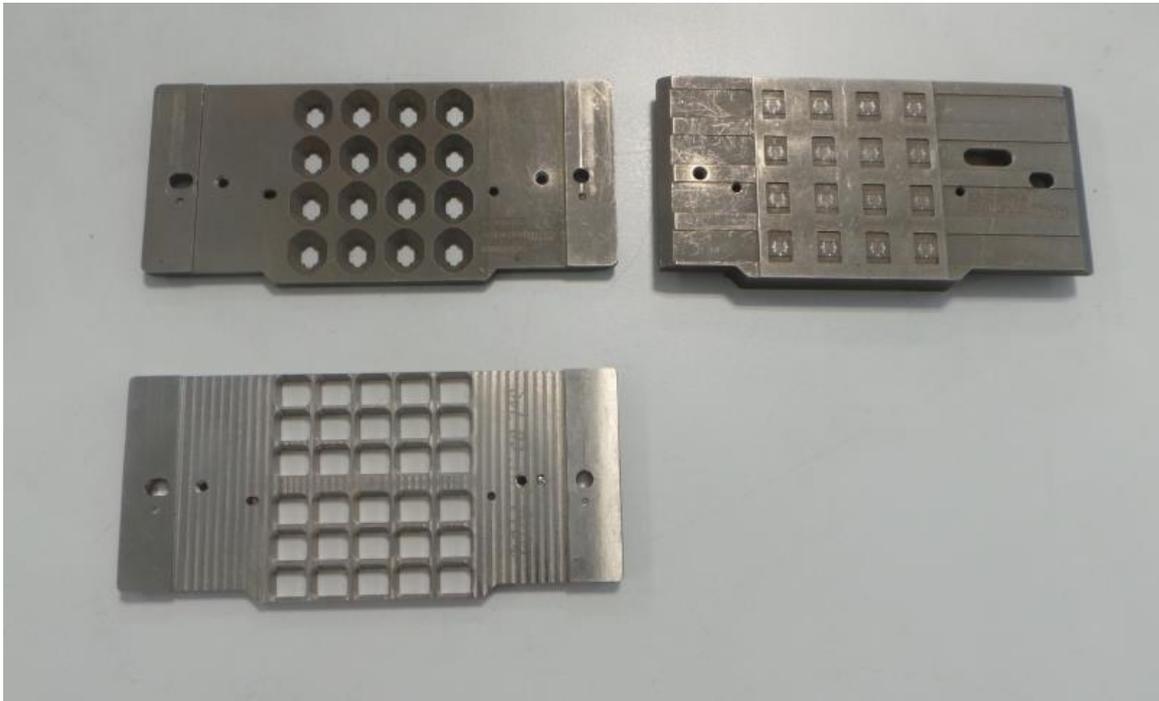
Оснастка для разварки проволочных контактов на установке iHawk. Вверху – фирменная оснастка, внизу – изготовленная дополнительно для другого типа корпусов
